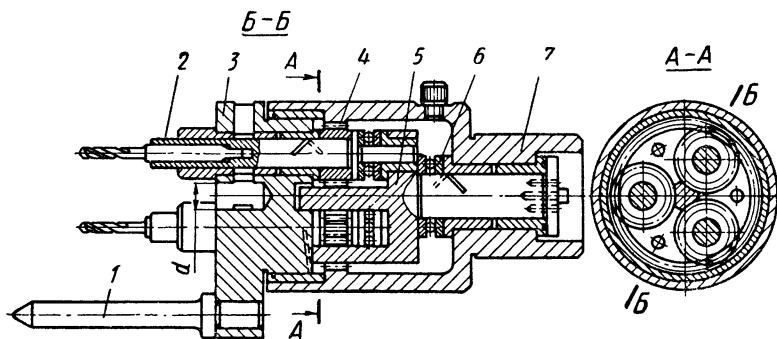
Многошпindleльная сверлильная головка к револьверному станку
